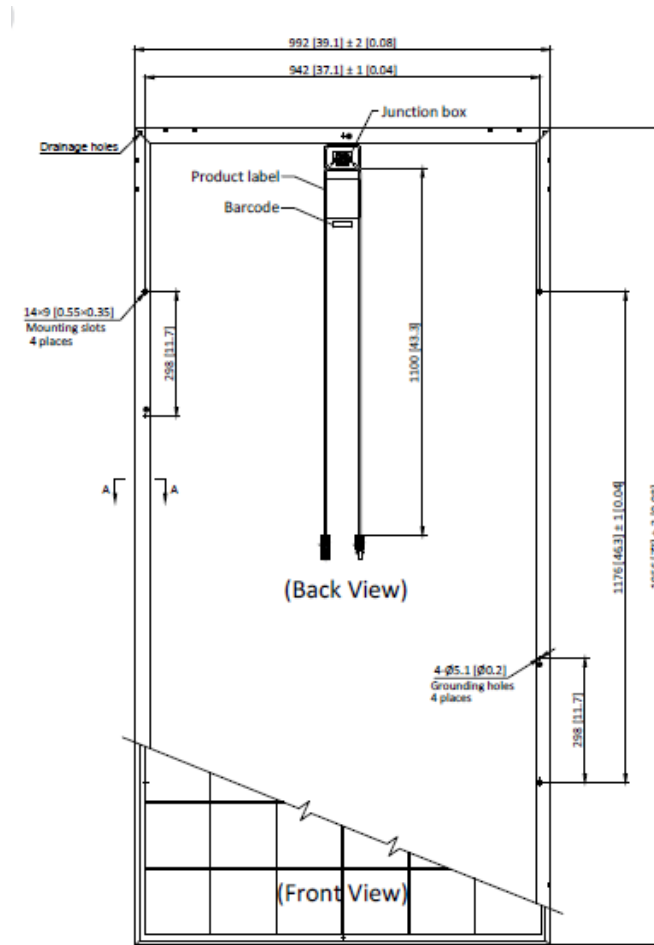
Vista genérica de la construcción del módulo fotovoltaico. Fuente: Ficha técnica módulo FV.
